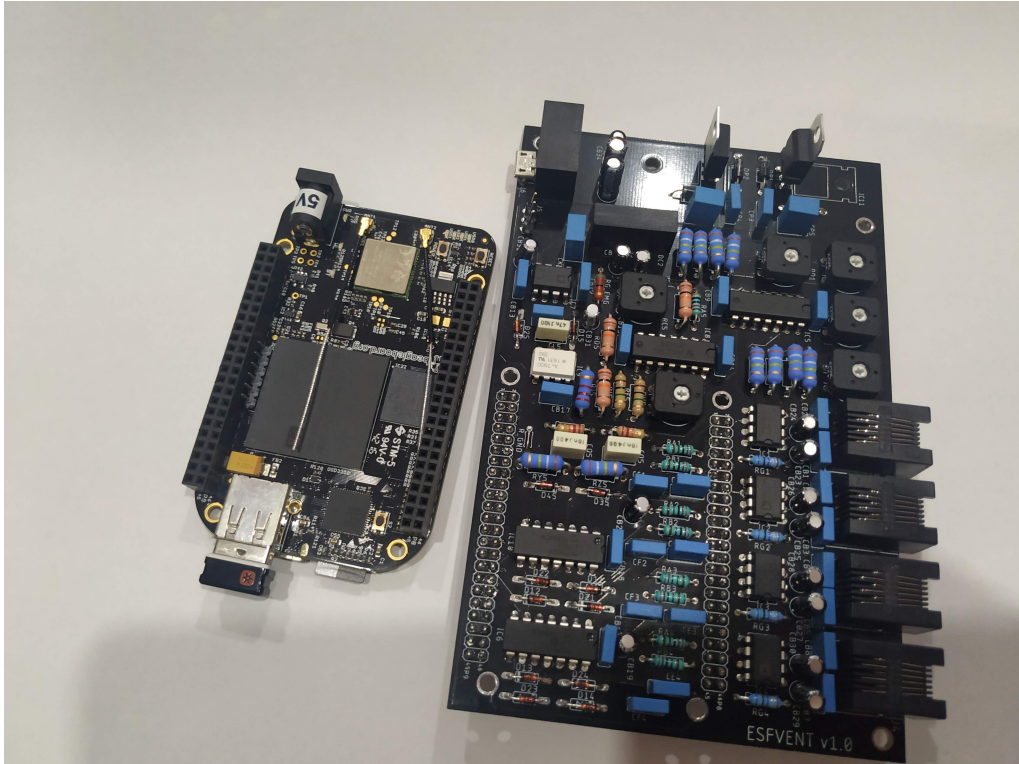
Fotografía de la placa montada sobre BeagleBone Black 2.
